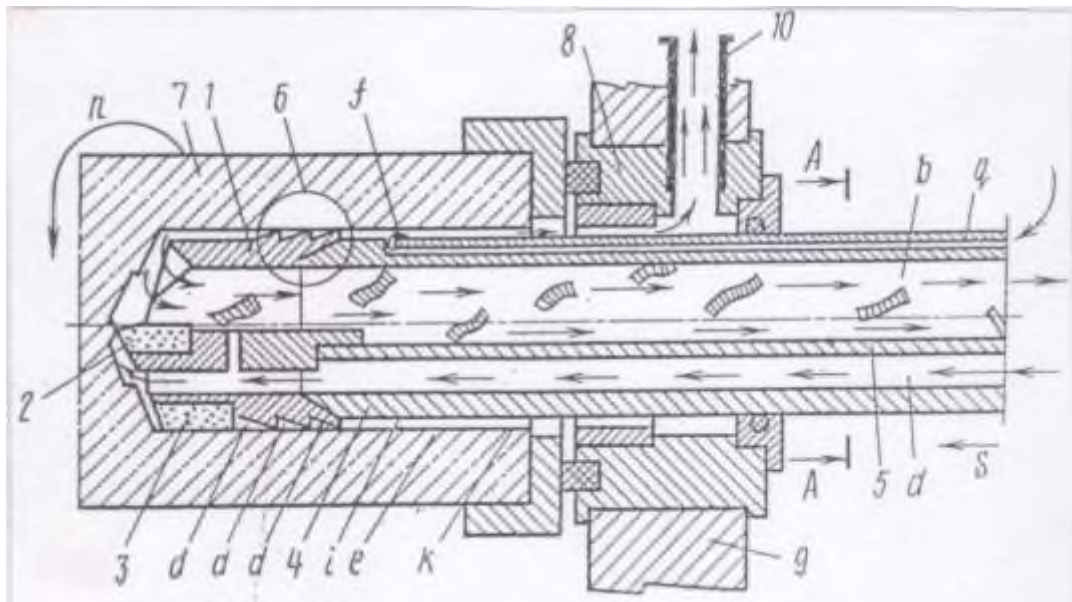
Загальний вид комбінованого інструменту (розріз)
